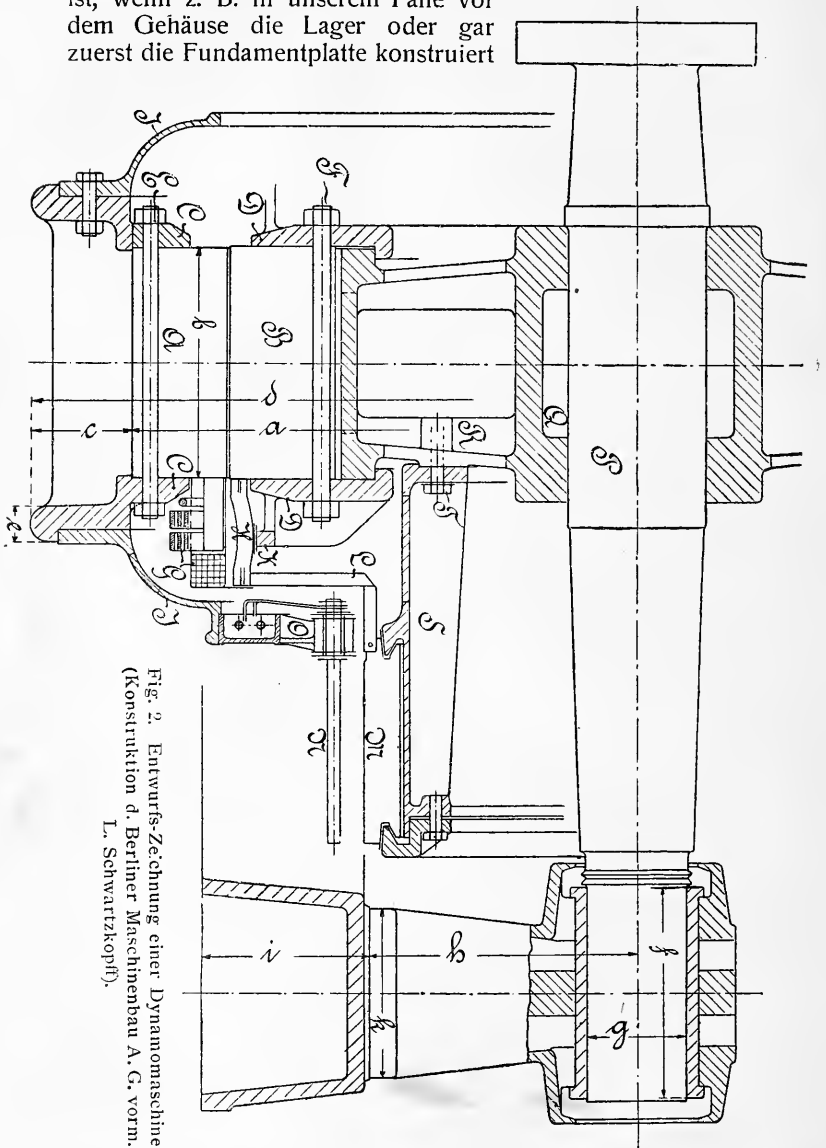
Entwurfs-Zeichnung einer Dynamomaschine
